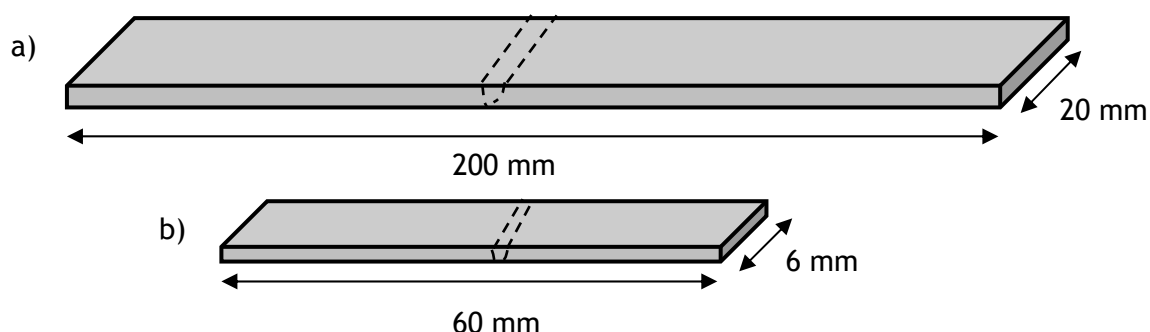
Modelo de provetes de tracção utilizados e respectivas dimensões. a) Provetes retirados das soldaduras efectuadas por processos GMAW; b) Provetes retirados das soldaduras laser.
